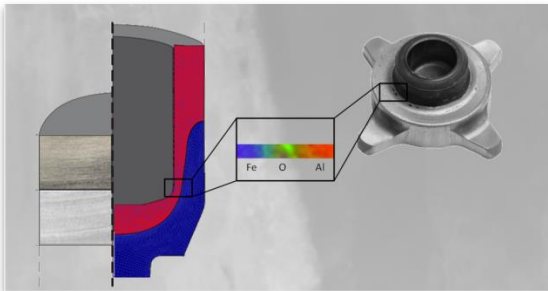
Kaltfließpressschweißen von Stahl und Aluminium
